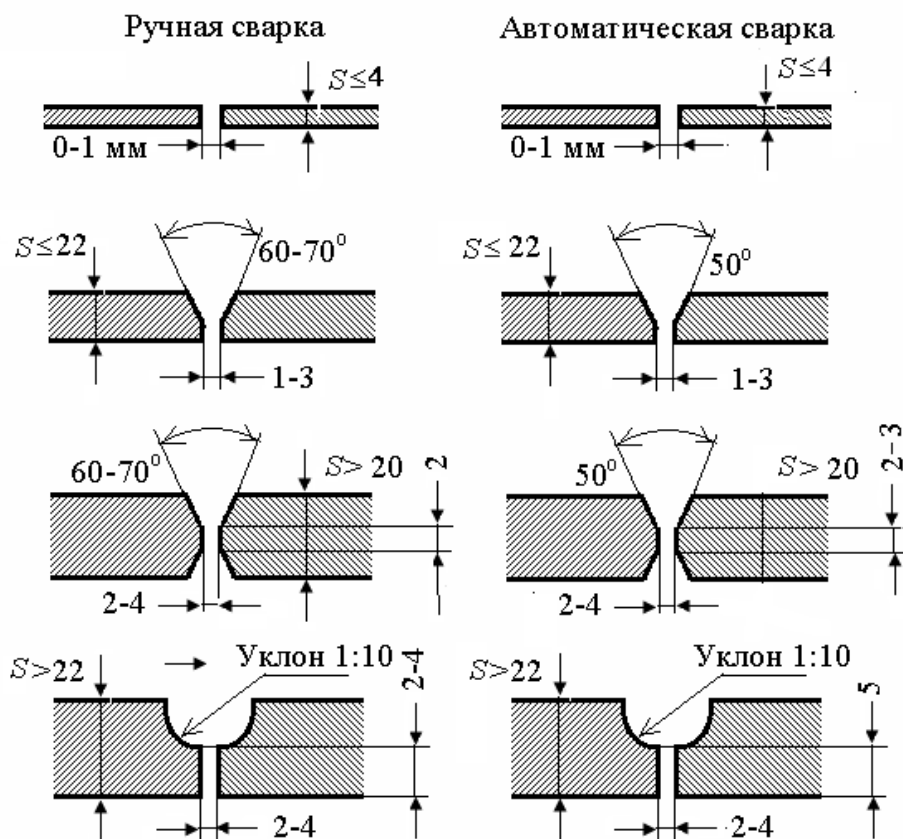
формы подготовки кромок под сварку при ручной дуговой и автоматической сварке под флюсом
